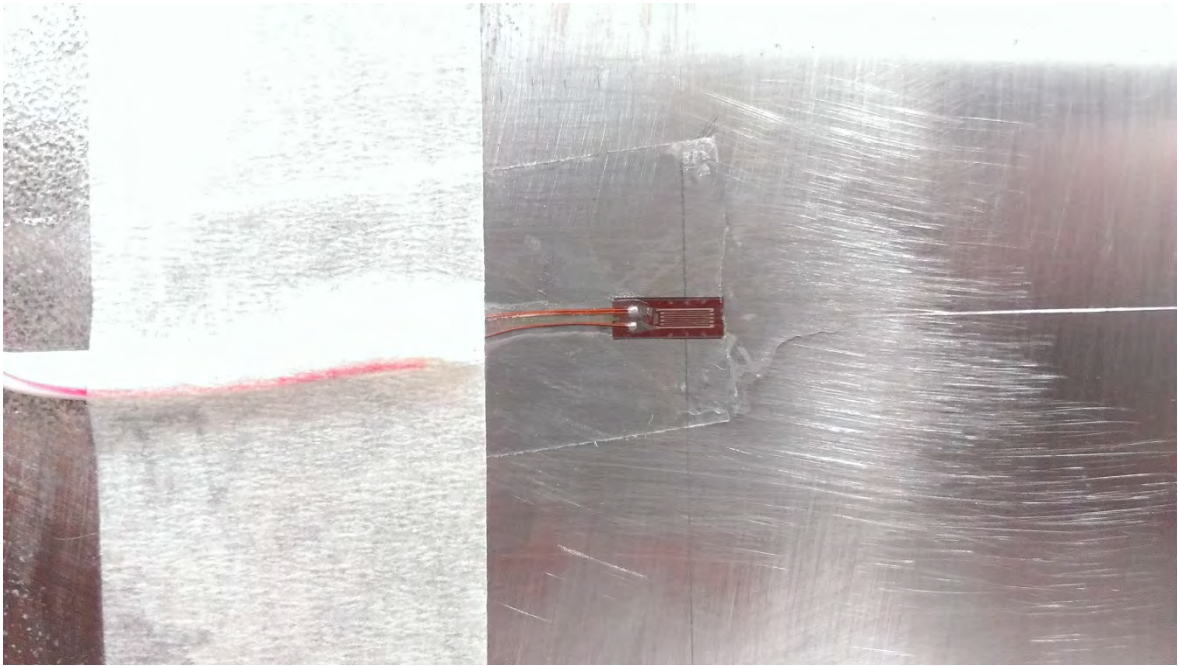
Dettaglio dell'estensimetro incollato nella faccia inferiore del braccio.
